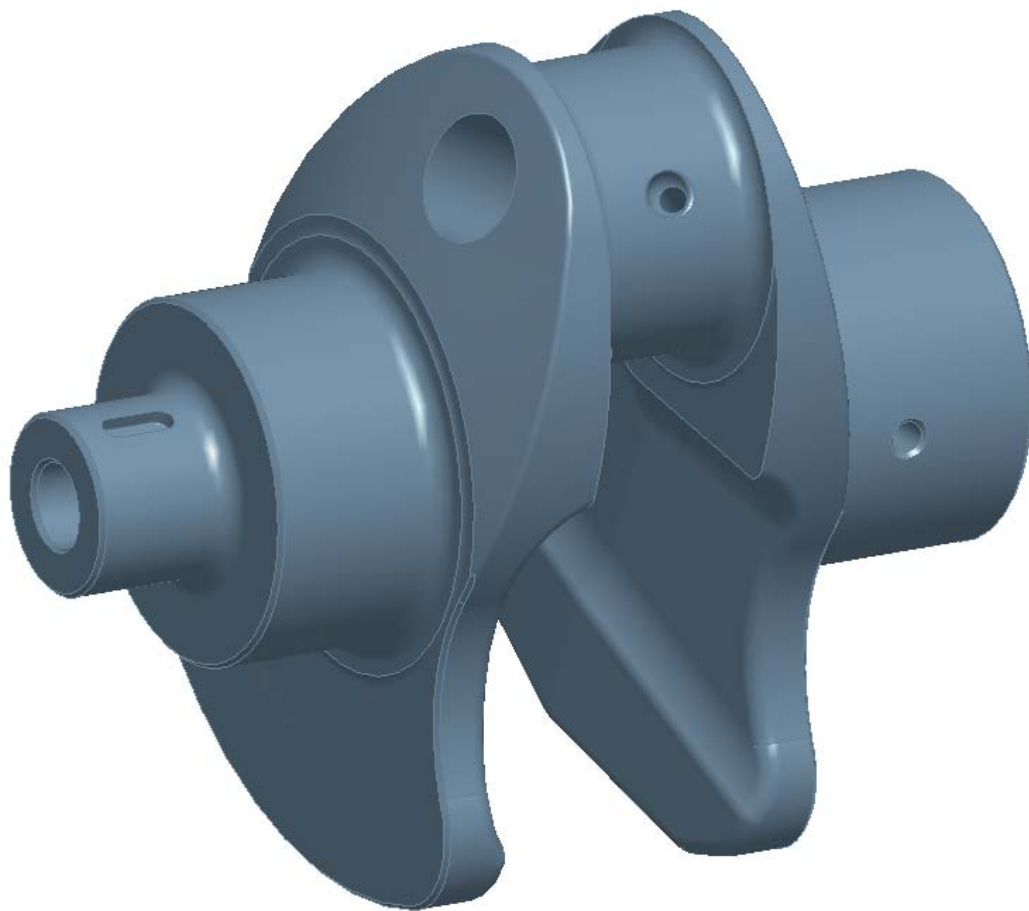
Klikový hřídel motoru Zetor UŘ III.
